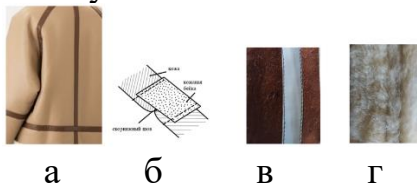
Скорняжный шов с настрочной кожаной бейкой: а) внешний вид соединения в готовом изделии; б) схема соединения; в) экспериментальный образец соединения деталей двухсторонней овчины со стороны кожной ткани; г) экспериментальный образец соединения деталей двухсторонней овчины со стороны волосяного покрова
